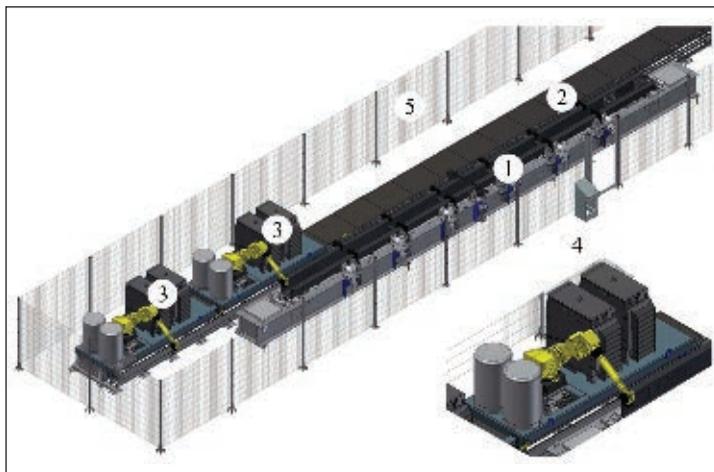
Установка для сварки внутреннего шва хребтовой балки: 1 — стенд; 2 — транспортная система; 3 — платформы с роботами и сварочными источниками питания; 4 — пульт управления; 5 — ограждение
